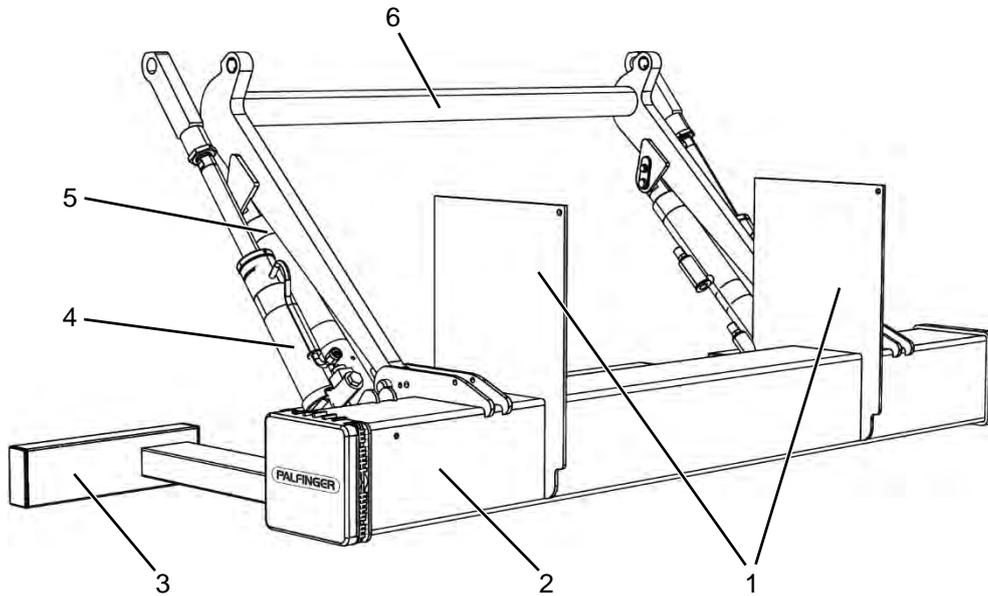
Trampilla elevadora con ménsulas de soldadura y grupo enchufable
